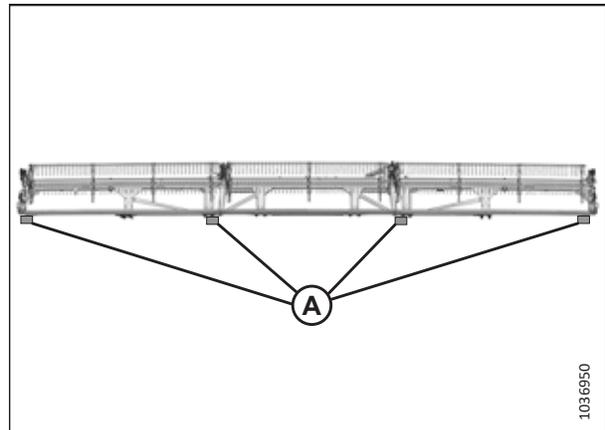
Blocs à chaque extrémité de la barre de coupe
